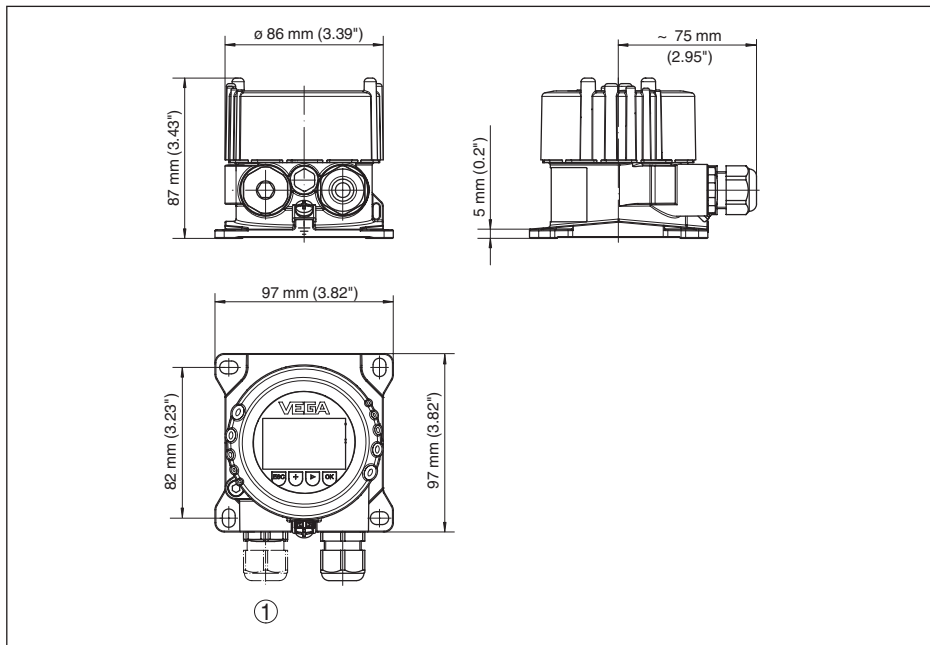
VEGADIS 81 с литым корпусом из нержавеющей стали
